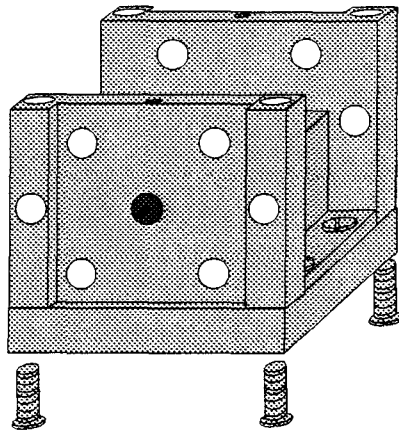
Des perles de verre sont soudées au centre des côtés
